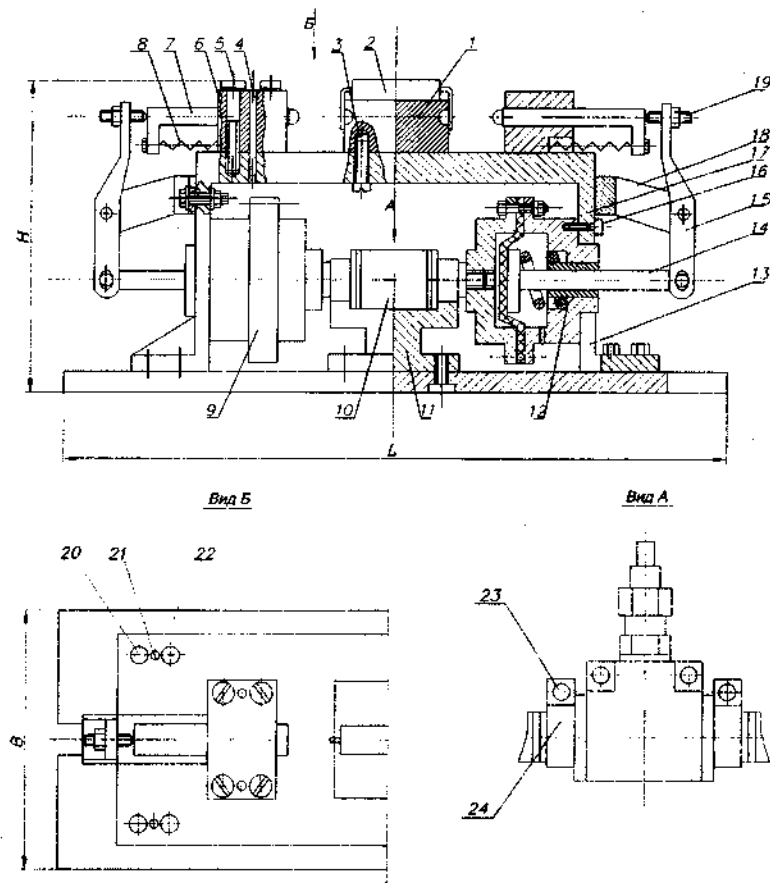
Конструкция приспособления для зиг-формовки ЭРЭ
